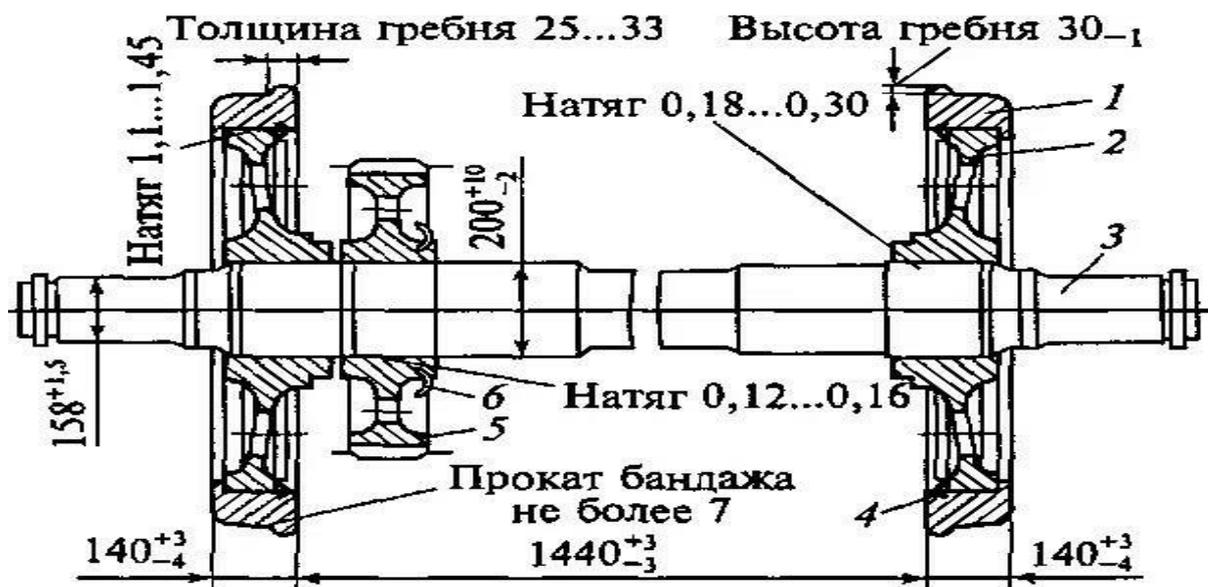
Колесная пара тепловоза: 1 - бандаж; 2 - колесный центр; 3 - ось; 4 - укрепляющее кольцо; 5 - ведомое зубчатое колесо; 6 - отбойное кольцо
